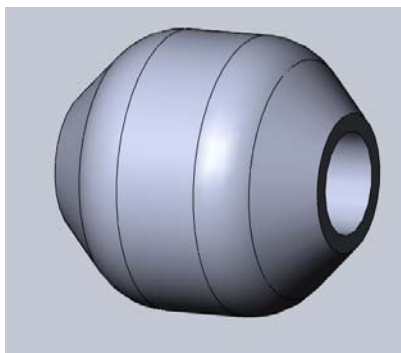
Модель выглаживающего инструмента бочкообразной формы
